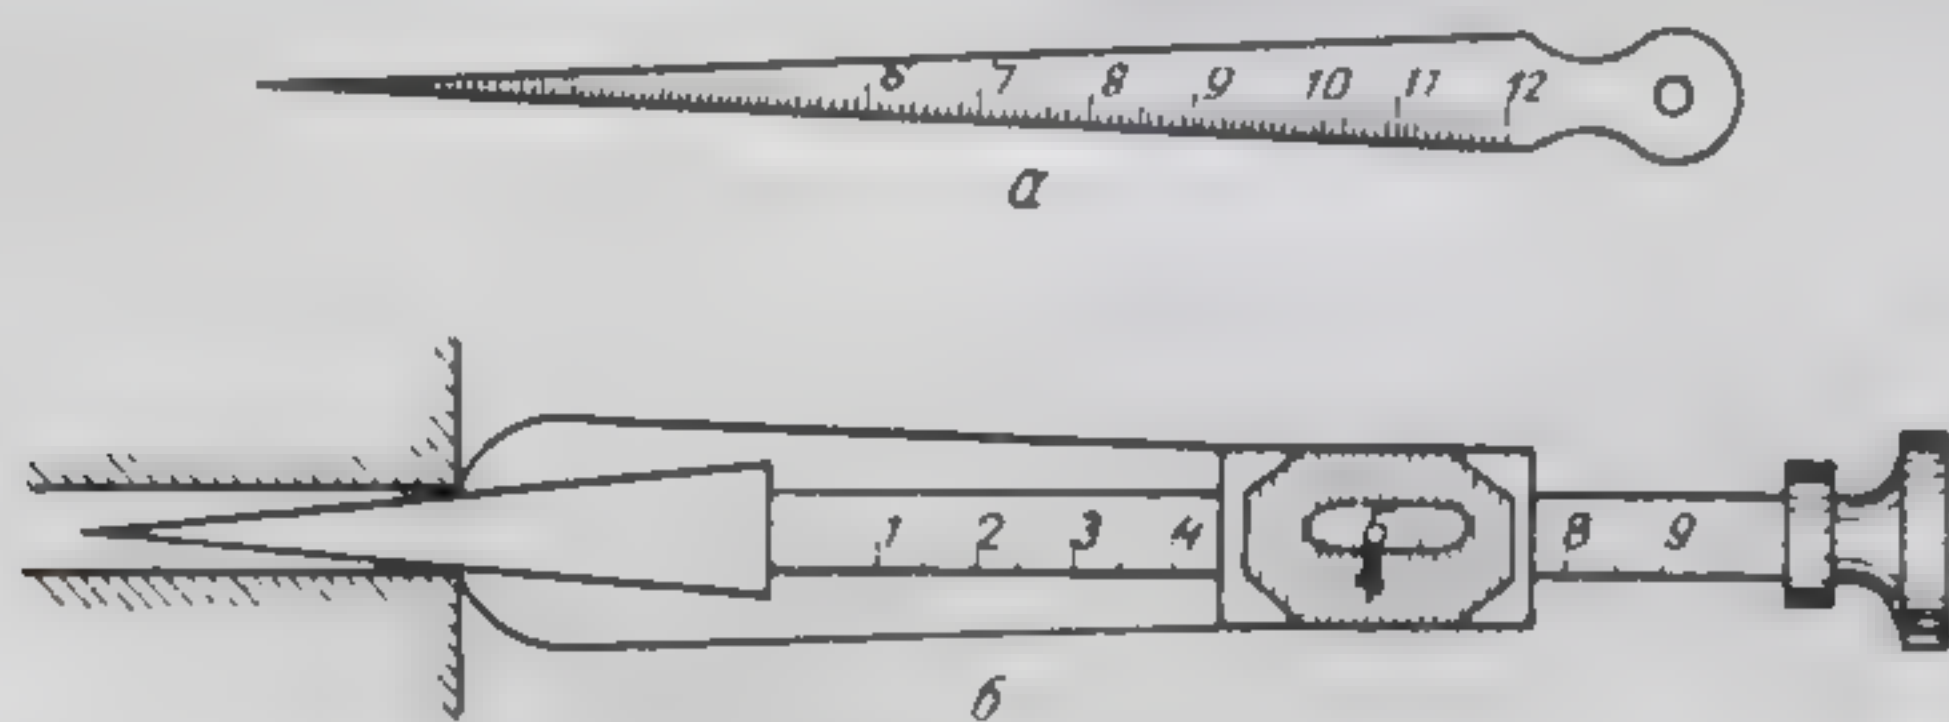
а — масштаб для измерения отверстий, б — конусный калиброметр
